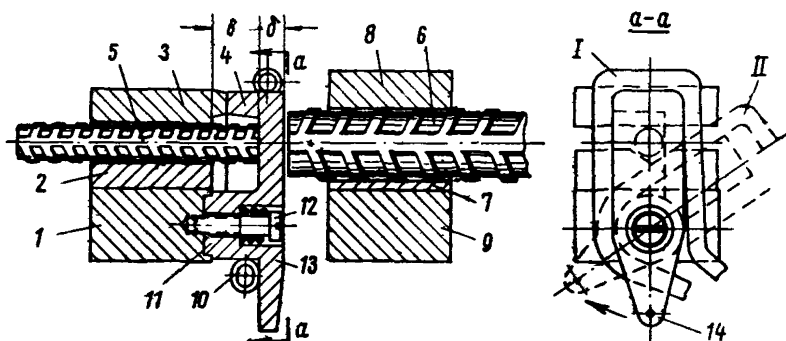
Схема модернизации серийной контактной стыковой машины для сварки стержней разных диаметров
